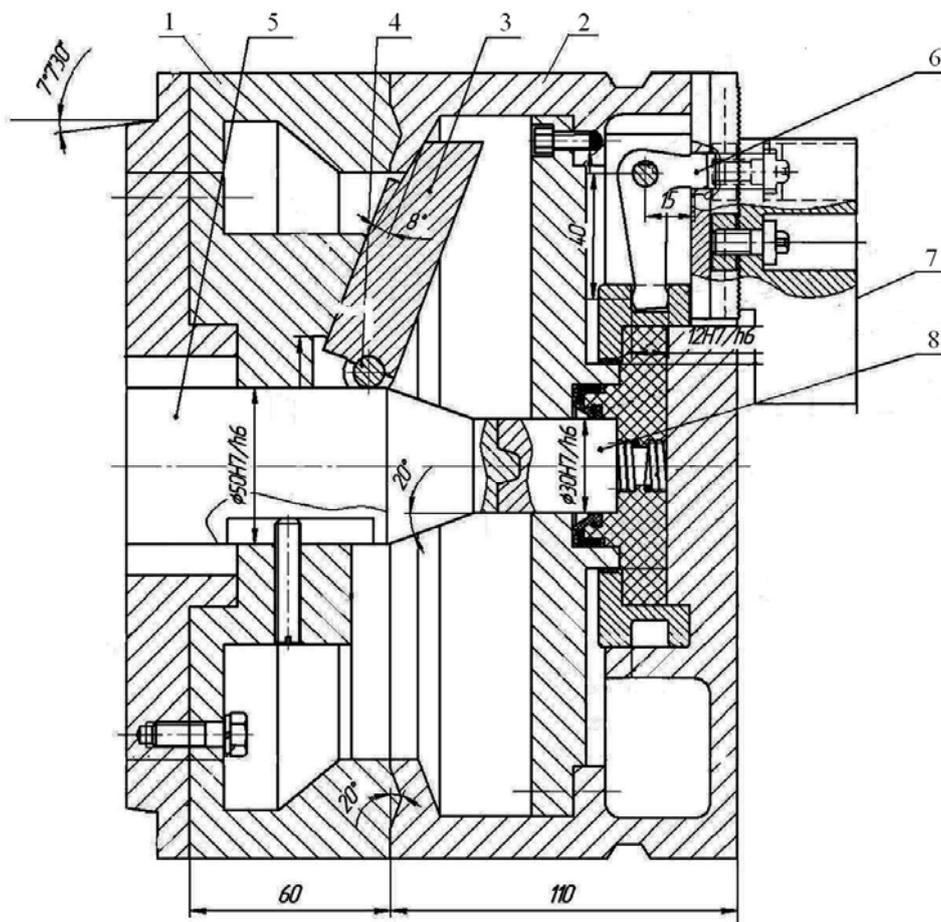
Патрон токарный с механическим закреплением наладок и гидропластмассовым устройством закрепления заготовок
